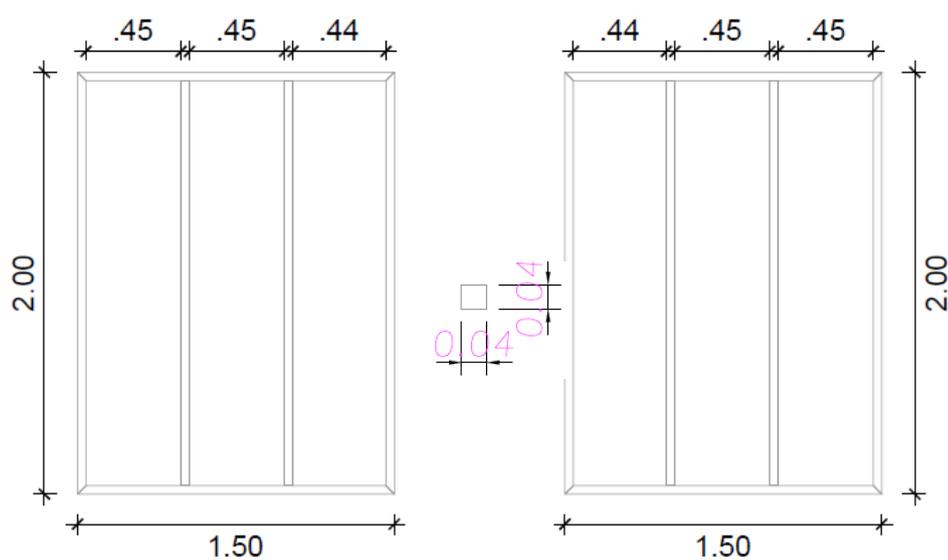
Vista frontal armado de puerta batiente a doble hoja con tubo cuadrado.
